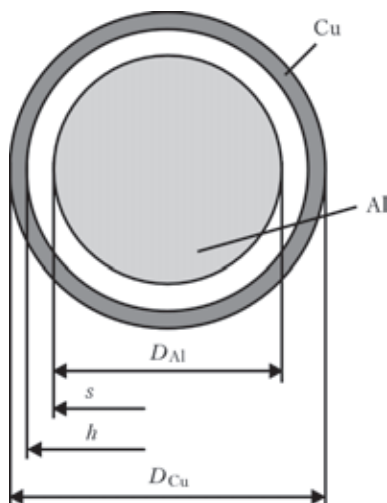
Параметры коаксиальной заготовки под сварку взрывом
